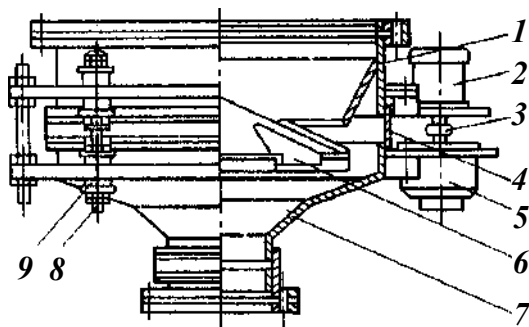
Вибрационный дозатор с активатором: 1 – корпус; 2 – электродвигатель; 3 – муфта; 4 – рукав; 5 – вибратор; 6 – активатор; 7 – вибрирующее днище; 8 – подвески; 9 – резиновый амортизатор.
